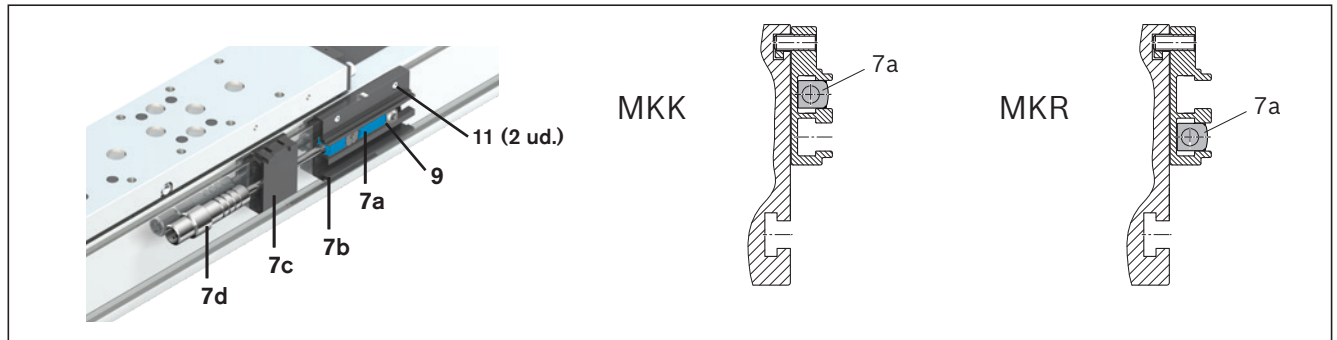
Montaje del sensor magnético (MKK/MKR-040-NN-3)
